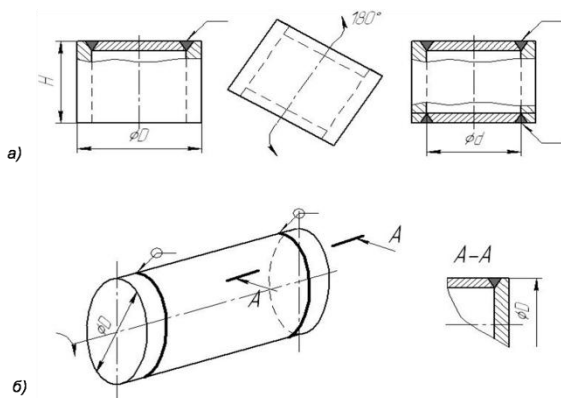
Варіанти зварювання днищ циліндра:
